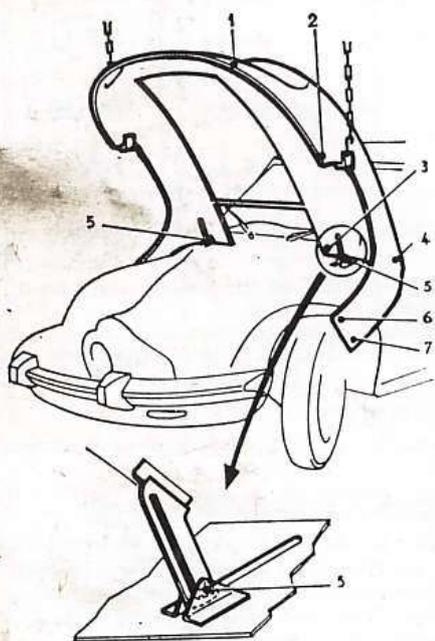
Ensemble de proue levé soutenu par des chaînes et détail d'une charnière.
